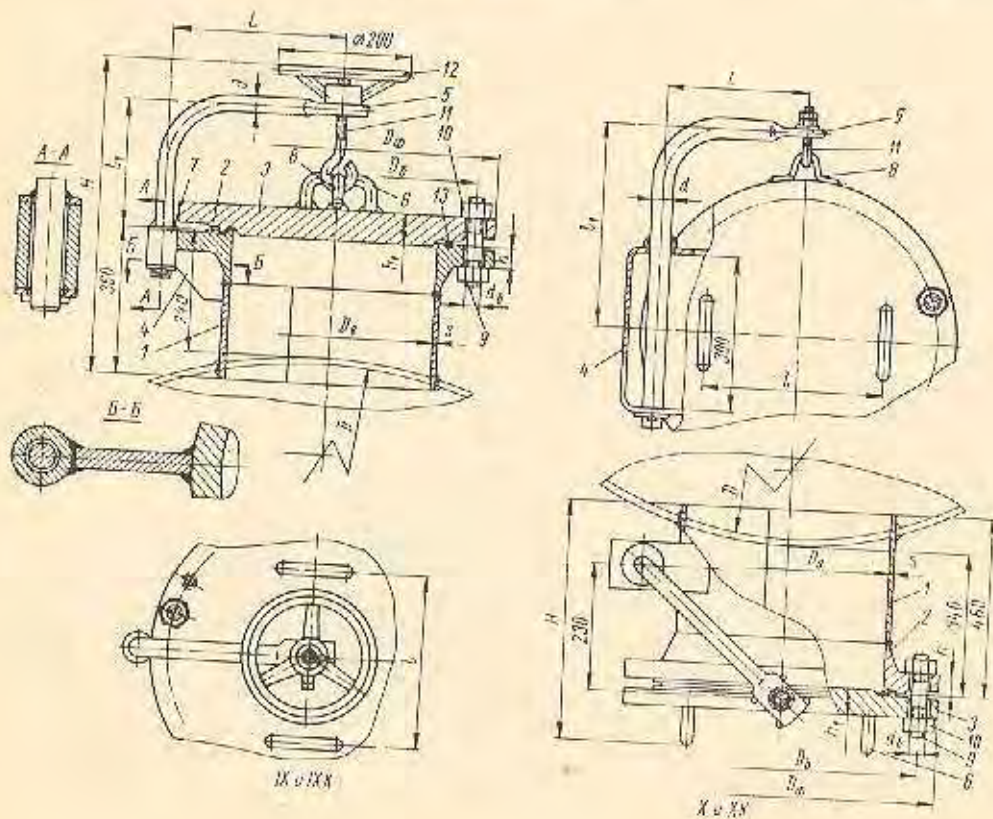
Конструкция люка с плоской круглой фланцевой крышкой и подъемно-поворотным устройством для сварных аппаратов на $P_n = 4$ МПа/м² (тип IX, IХК, X и ХК по ОН 26-01-10-65).
